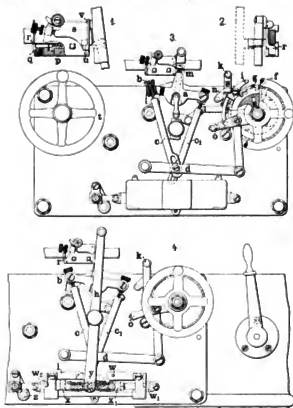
Z. A. Universal-Steig-/Kondensmaschine.
